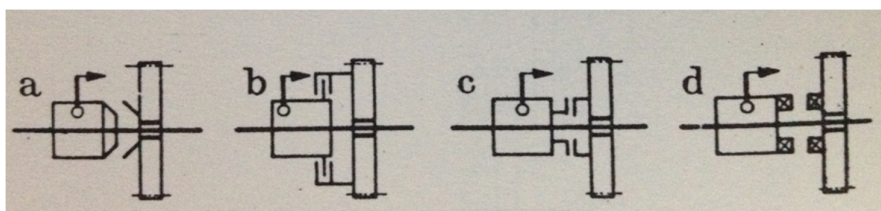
Engrenagens (a) fixas, (b) deslocáveis e (c) loucas.
